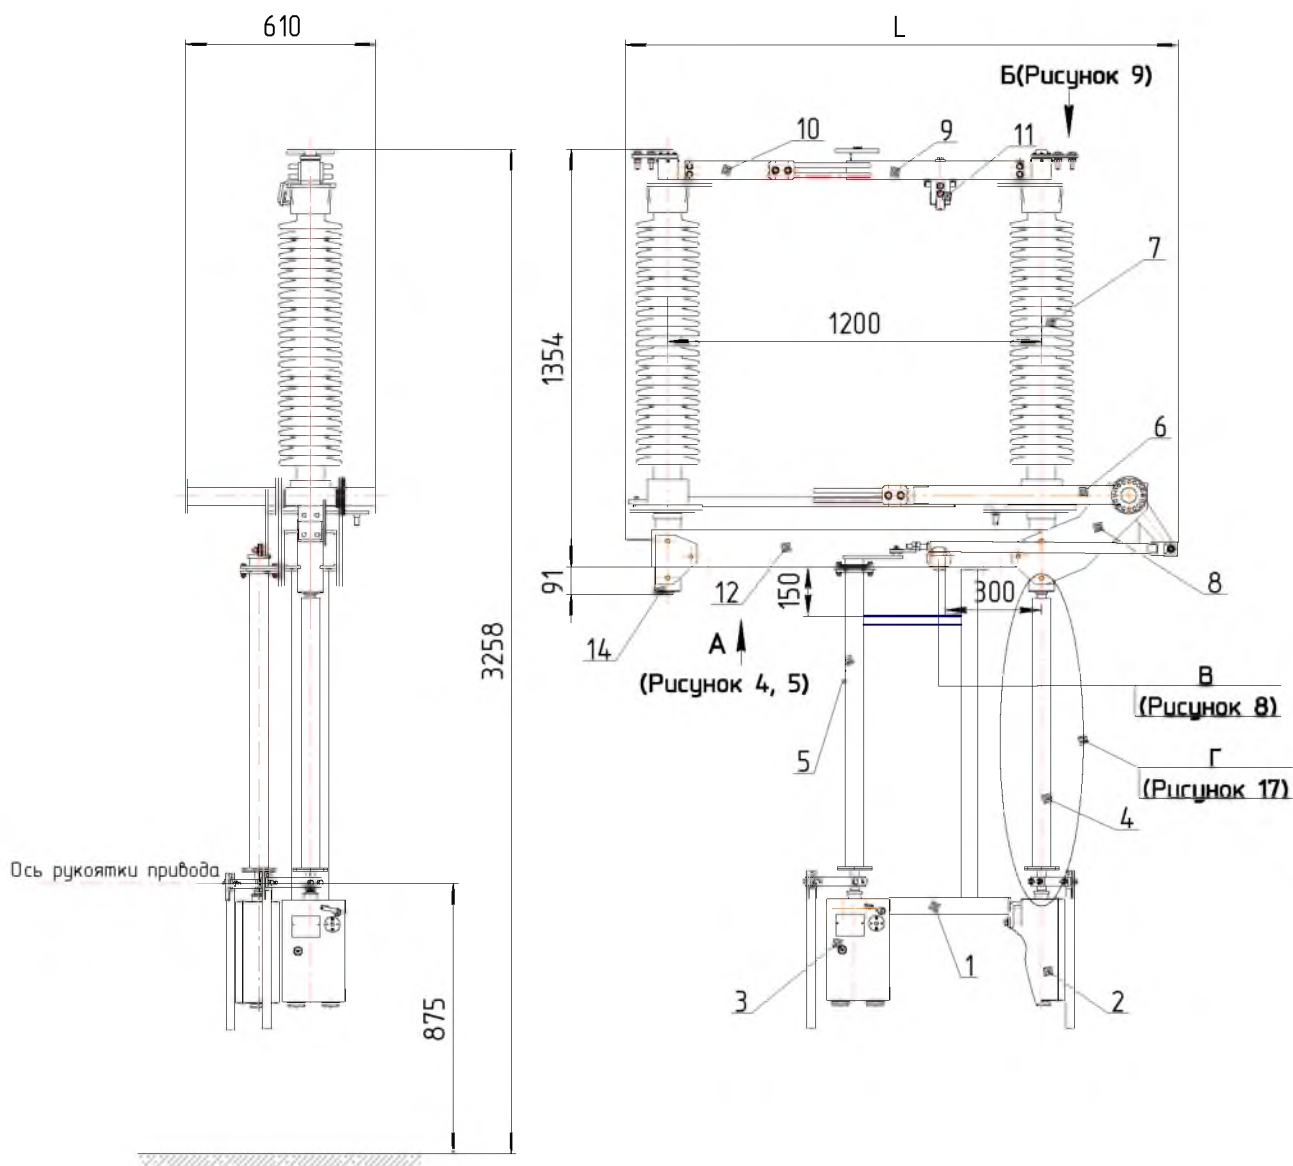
Однополюсный разъединитель РГП СЭЦ® -110/1250
